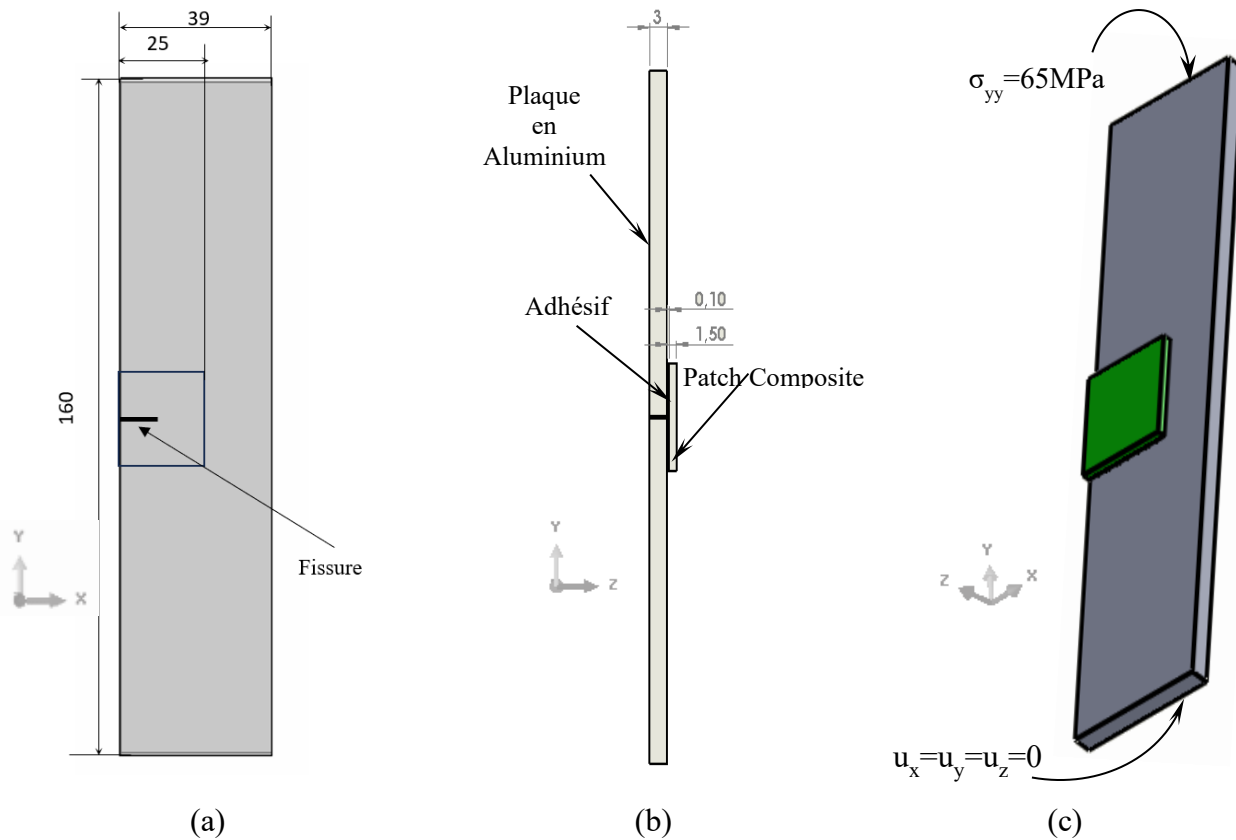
Géométrie de la plaque réparée (a) vue de face (b) vue de côté (c) vue en 3D [21].
